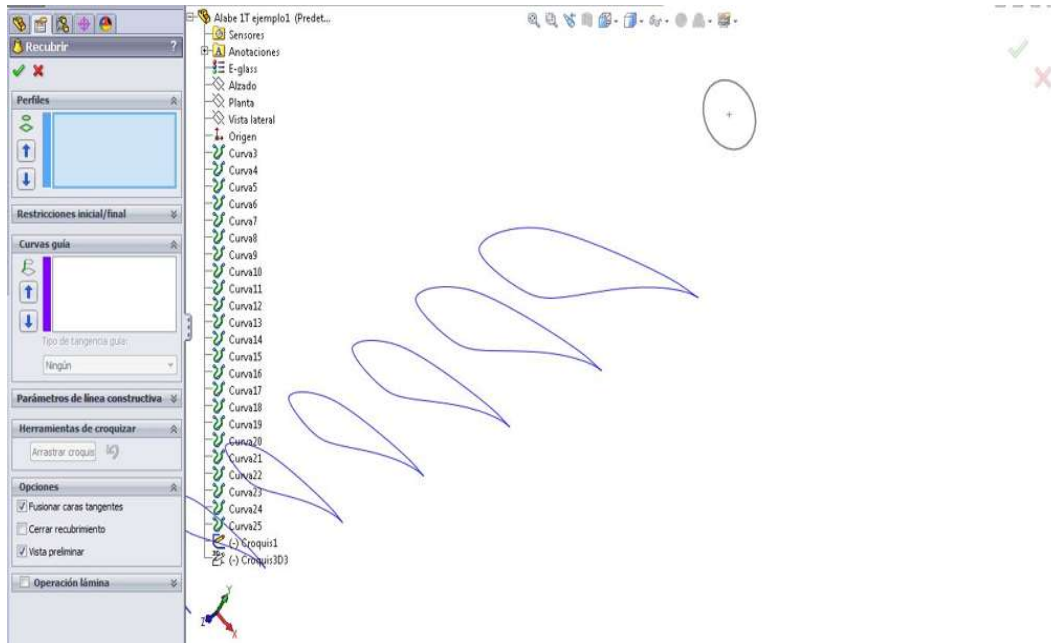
Herramienta recubrir en el sistema CAD en SolidWorks.
